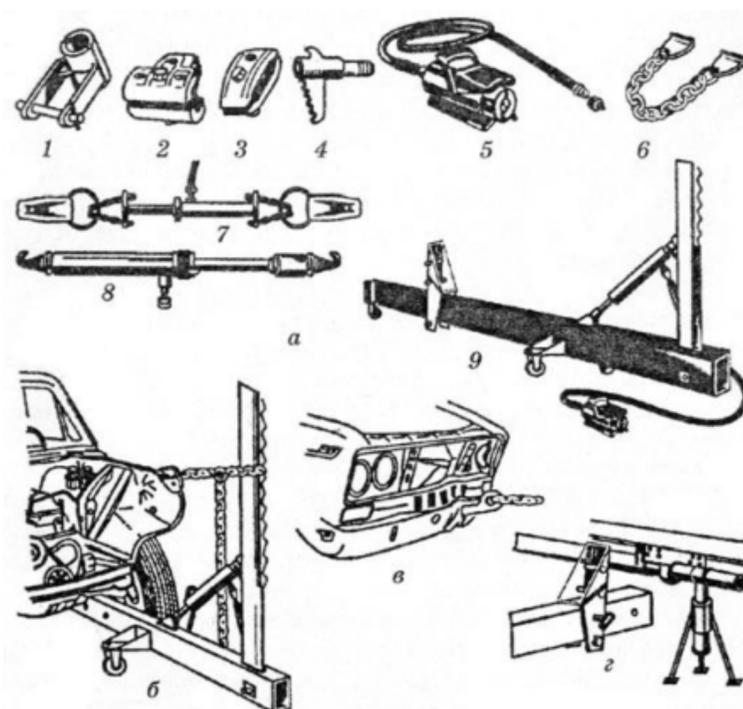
Приспособления для выполнения правки деформированного участка кузова:
